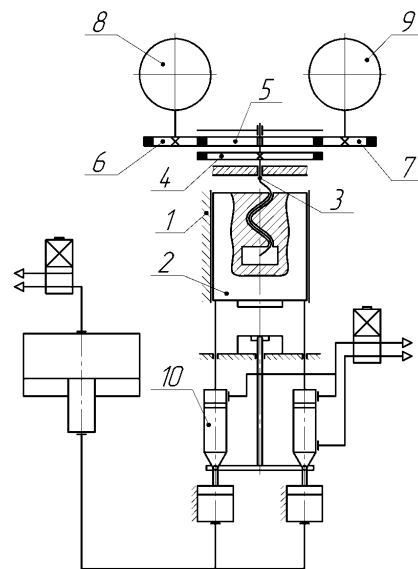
Кінематична схема гвинтового преса (1 – станина; 2 – повзун; 3 – гвинтовий шпindelь; 4 – ведений робочий маховик; 5 – ведучий маховик; 6, 7 – бокові ведучі маси; 8, 9 – електродвигуни; 10 – привід зворотного ходу повзуна)
